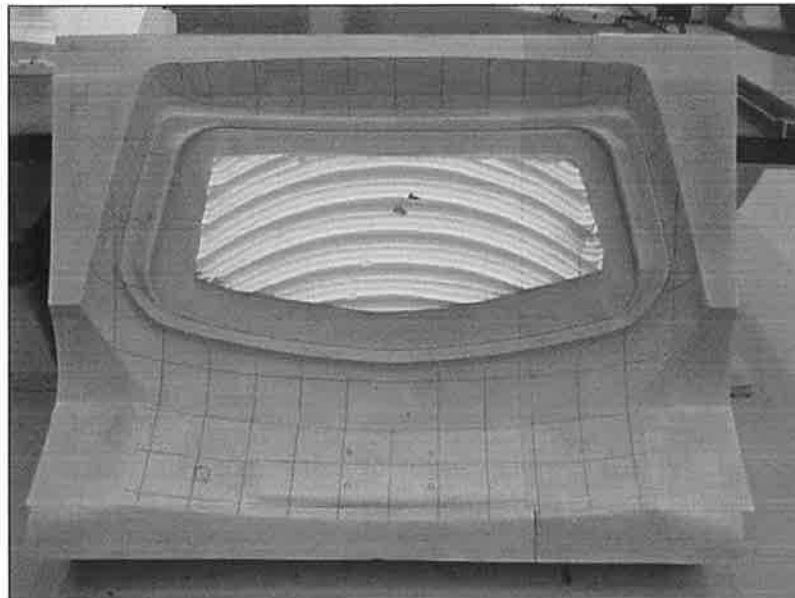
Molde usinado em negativo do painel externo da tampa traseira. (Macarrão, 2004).
